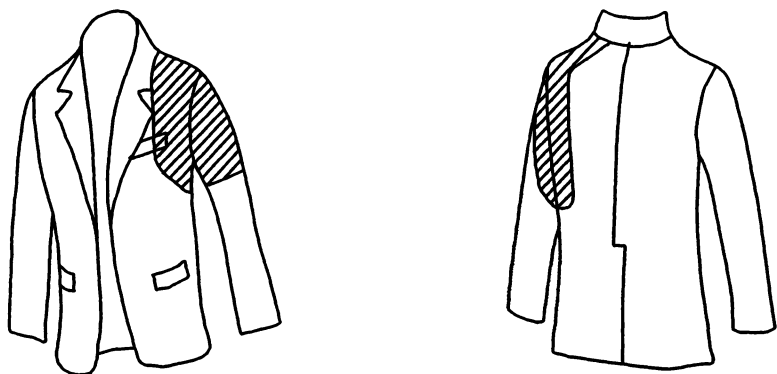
Схема расположения обрабатываемых участков левого оката, проймы и верхней части рукава
